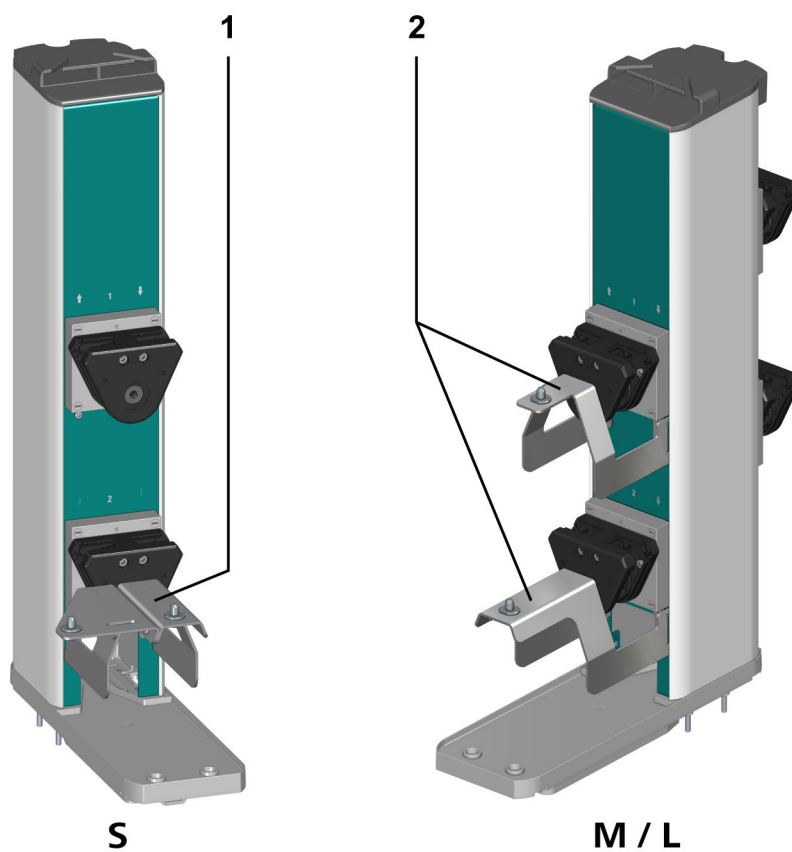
Parte frontal – módulo de bomba peristáltica com suportes para tampa
